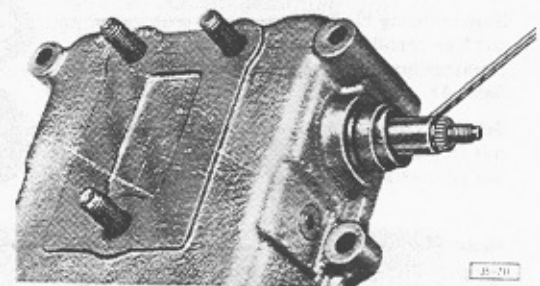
Dichtring für Schaltwelle mit Schraubenzieher ausziehen
